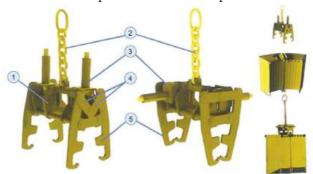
Устройство грузозахватное для коробок [7, с. 142]: 1 — основание; 2 — цепь; 3 — ручки в сборе; 4 — тяги; 5 — крюки
